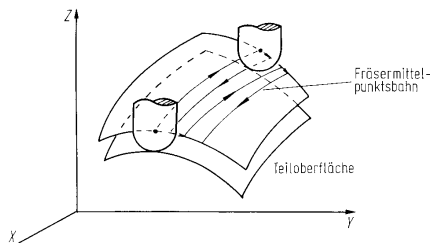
Fräsermittelpunktsbahnen zum Fräsen einer Werkstückoberfläche in den Achsen X, Y und Z
